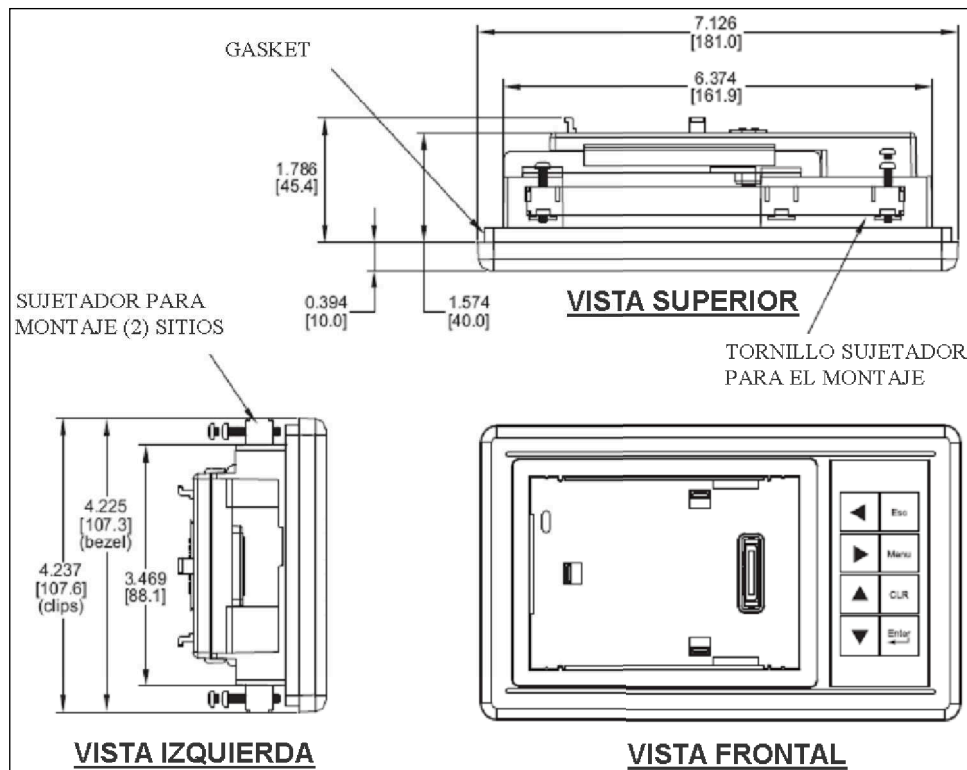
Dimensiones para el montaje del panel EA-MG-BZ1⁷²
